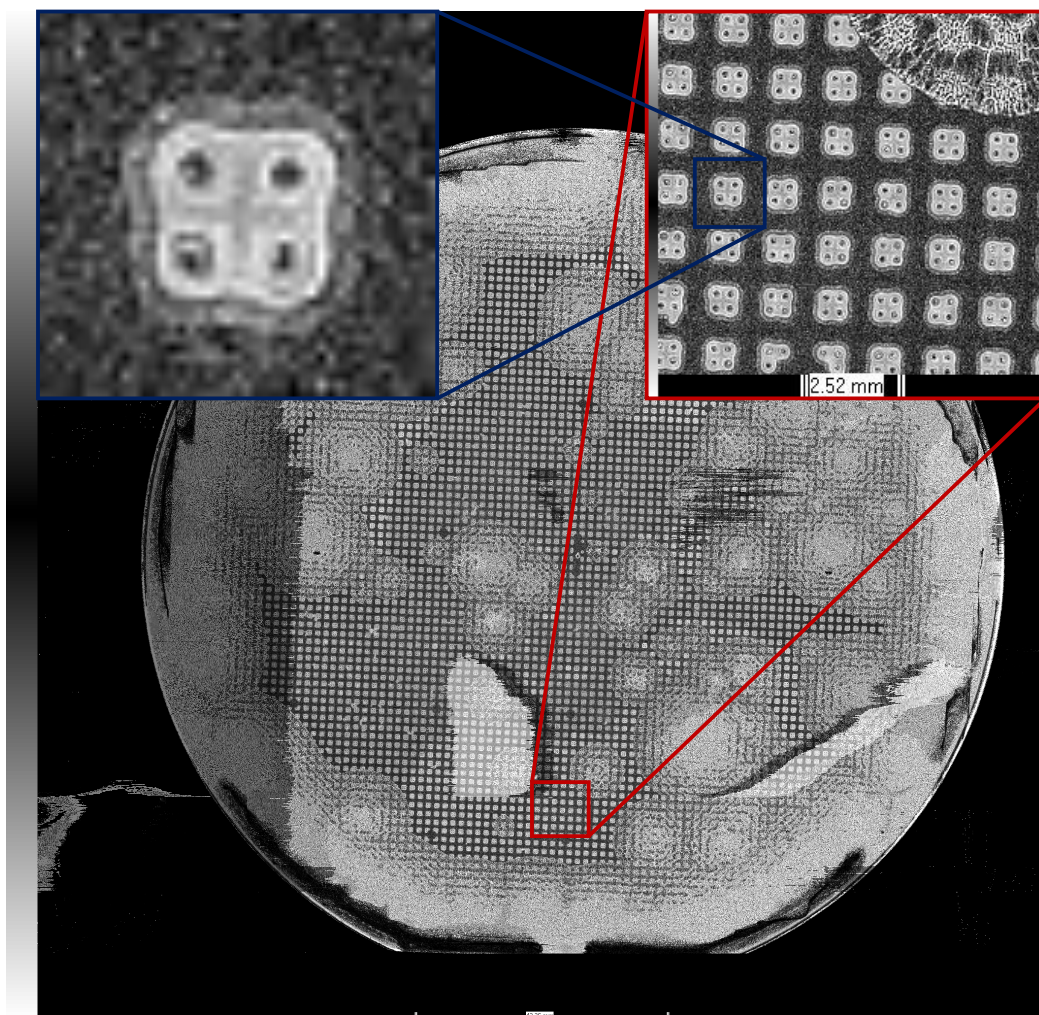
Image SAM du test de collage avec des piliers #3 sur des tranches de 150 mm. La mesure est bruitée, mais montre tout de même la présence de nombreux défauts dans le collage.
